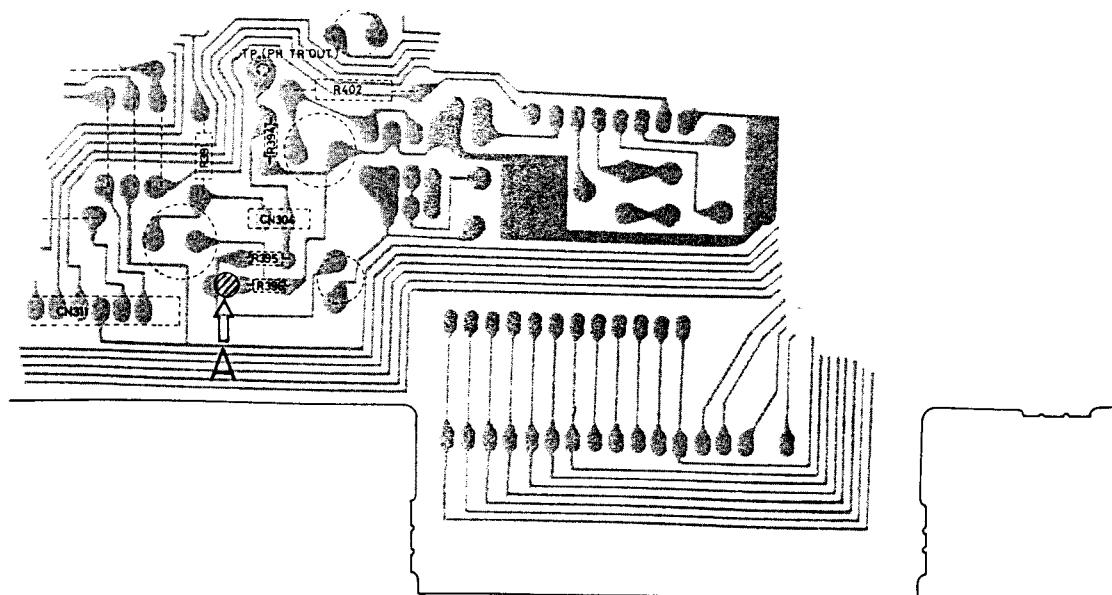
Lieux de réglage (côté feuille de l'ensemble matriciel)
